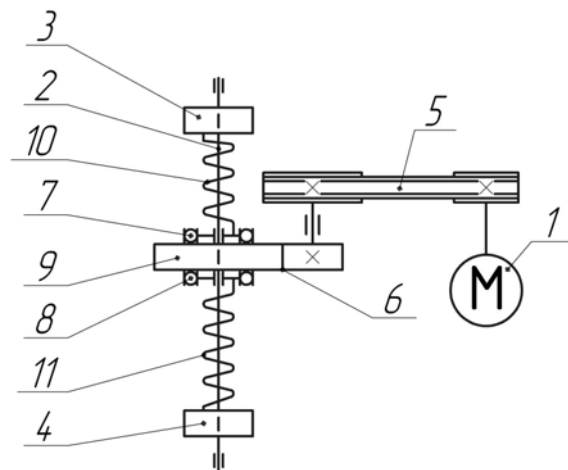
Кінематична схема привода круглов'язальної машини: 1 – електродвигун; 2 – вертикальний приводний вал; 3, 4 – шестерні; 5 – клинопасова передача; 6 – зубчаста передача; 7, 8 – обгінні муфти; 9 – зубчасте колесо; 10, 11 – пружини кручення
